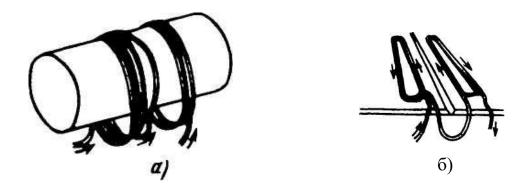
Схема размещения сварочных кабелей при размагничивании (стрелками указано направление тока): а - при сварке трубопровода; б - при сварке листовых конструкций
